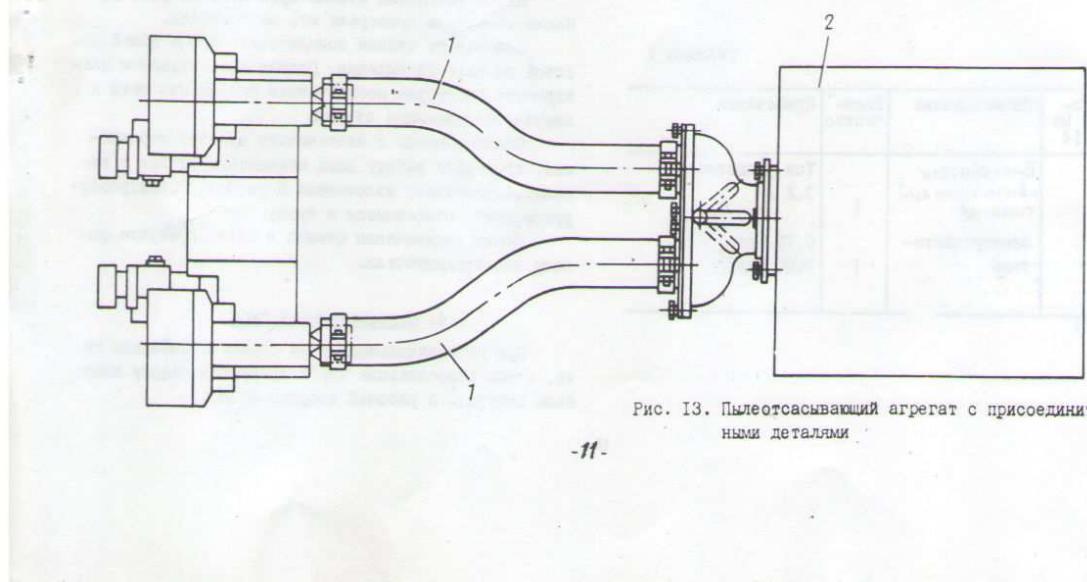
Пылеотсасывающий агрегат с присоединительными деталями
